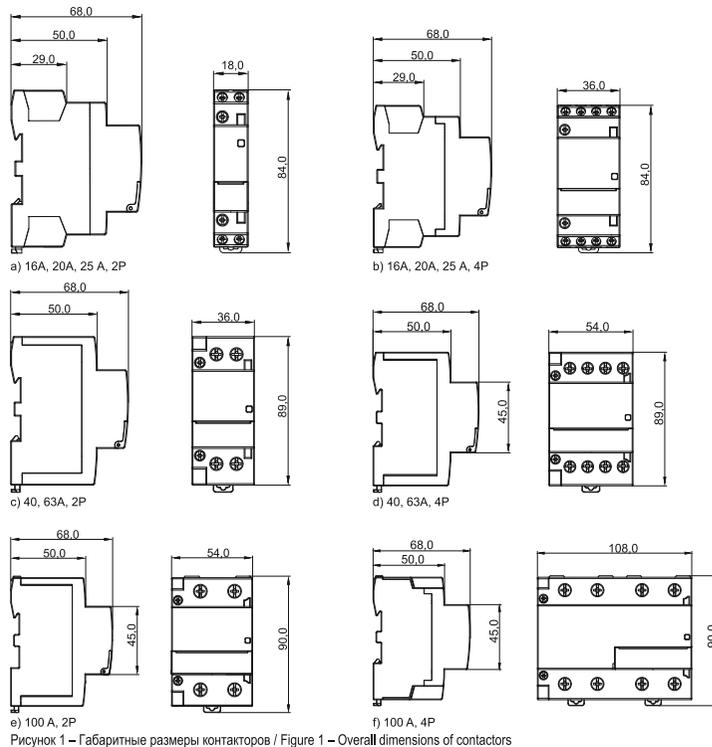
Габаритные размеры контакторов / Figure 1 – Overall dimensions of contactors
